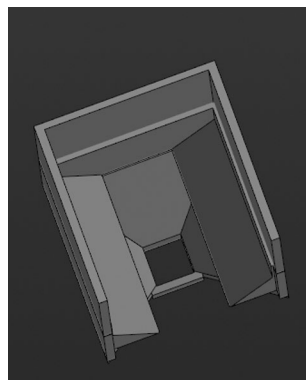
3D-модель мехатронного загрузчика (вид № 2)
